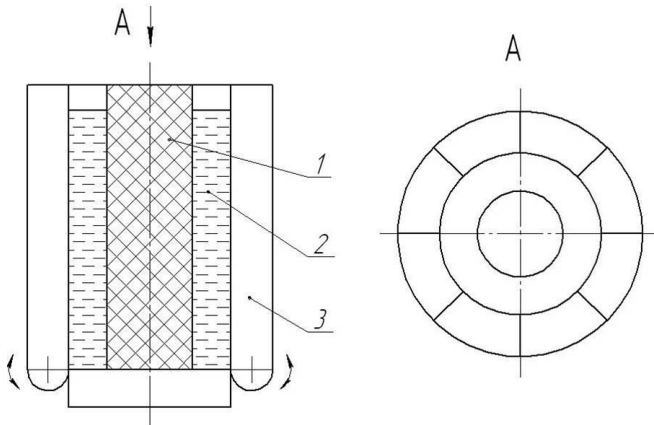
Спрощена конструкція стулкового кокілю:
